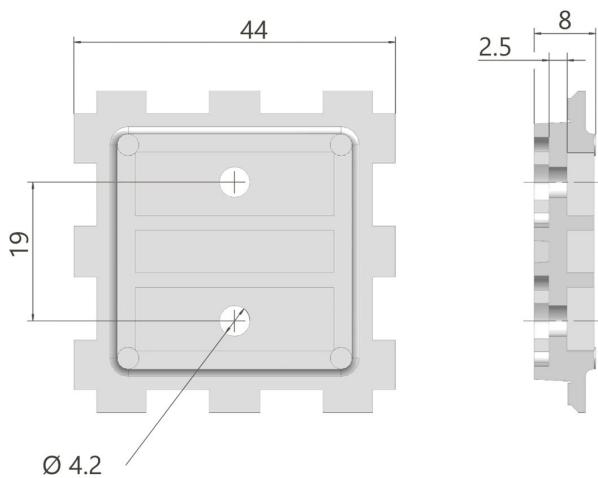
Piastra dell'adattatore: vista dall'alto e sezione
